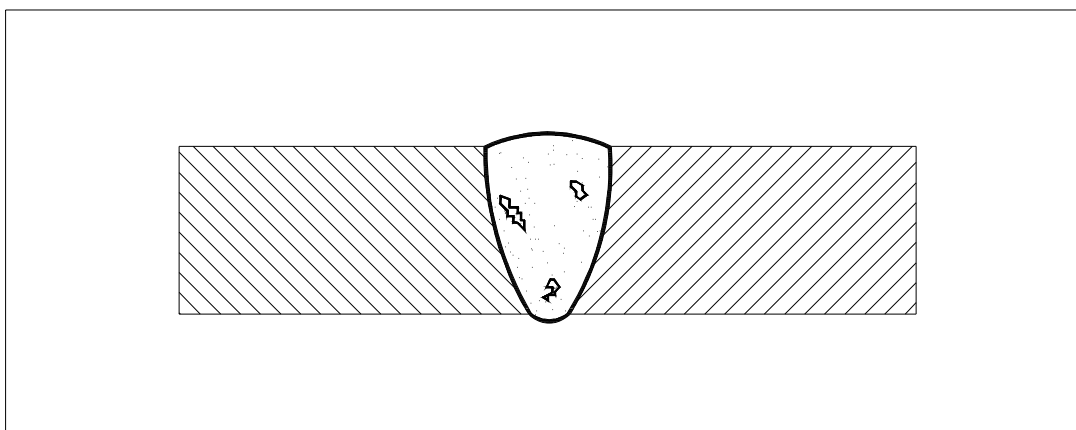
Inclusiones de escoria en una soldadura en V.
